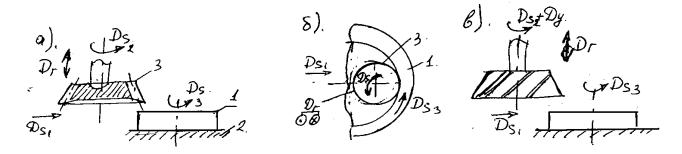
Схемы обработки зубчатых колес на станке мод. 514.
